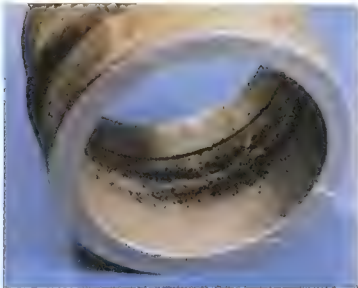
Кислотная коррозия у сварного шва
